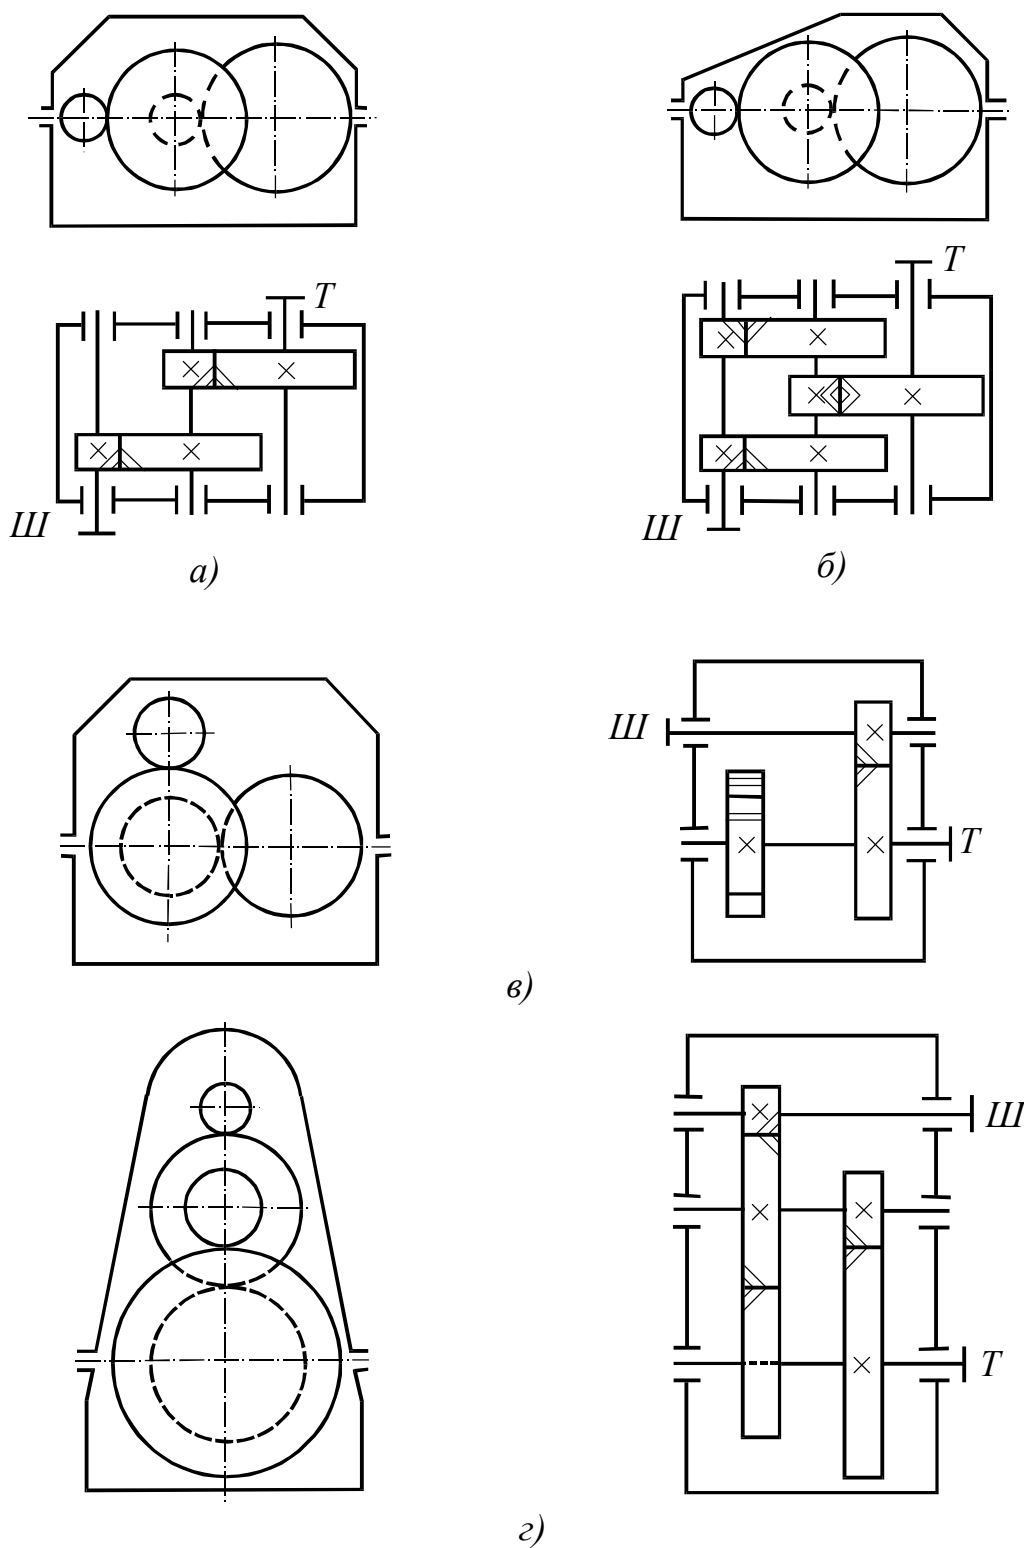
Кинематические схемы двухступенчатых редукторов
